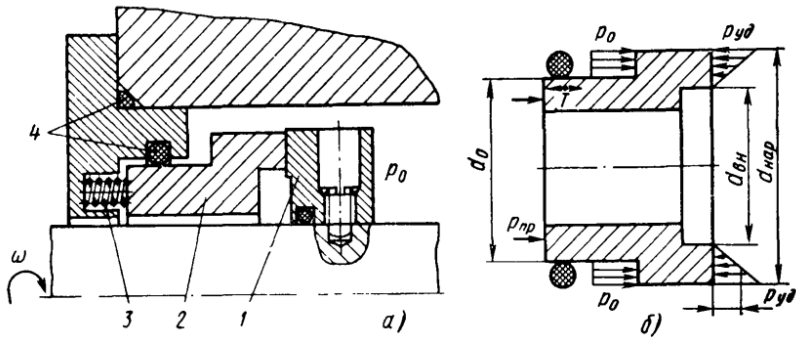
Конструкція торцевого ущільнення: 1 – роторна деталь; 2 – статорна деталь; 3 – пружина; 4 – кільця
